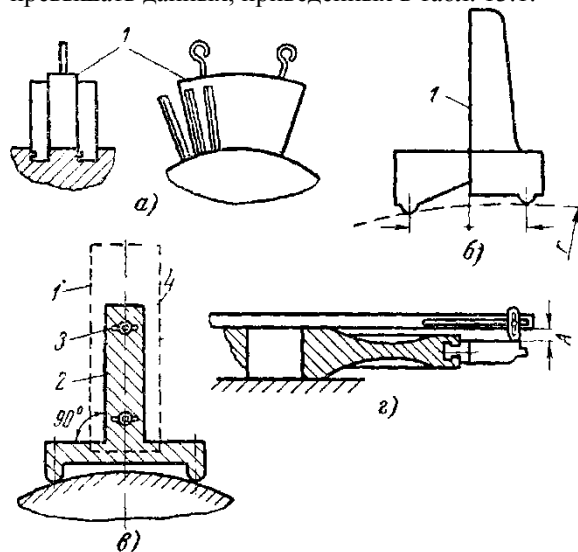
Шаблоны для проверки установки лопаток. а — для сборки лопаток реактивных ступеней, б и в — для проверки установки лопаток в тангенциальном направлении, 1—рабочая кромка шаблона, 2—держатель шаблона, 3—зажимной винт, 4 — настроечная планка, г — линейка и регулируемый указатель для проверки установки лопаток в аксиальном направлении на снятом диске.
